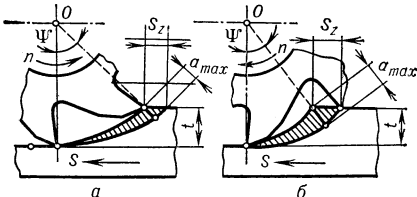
Схемы фрезерования: а — против подачи; б — по подаче.
